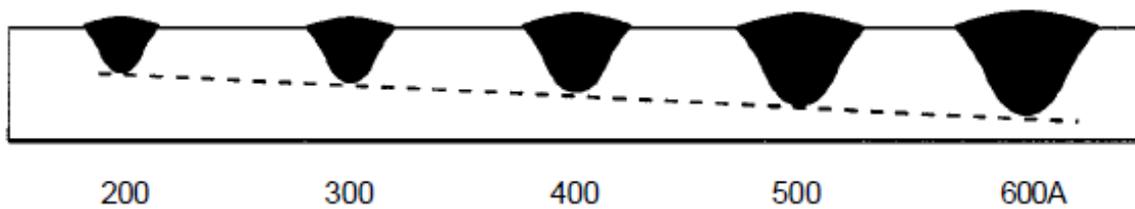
Effet du courant de soudage sur l'aspect de la soudure.
